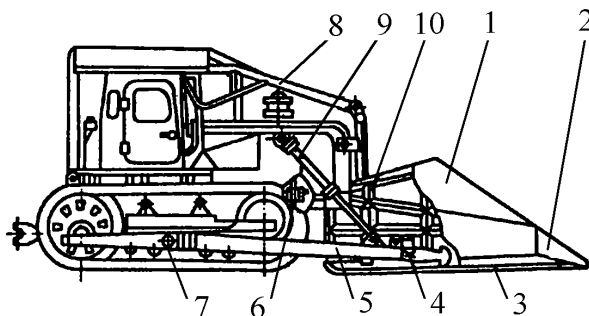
Кусторез ДП-24: 1 – отвал; 2 – носовой клин; 3 – нож; 4 – шаровая головка; 5 – толкающая рама; 6 – привод шлифовального диска; 7 – шаровые втулки; 8 – ограждение; 9 – гидроцилиндр; 10 – каркас
